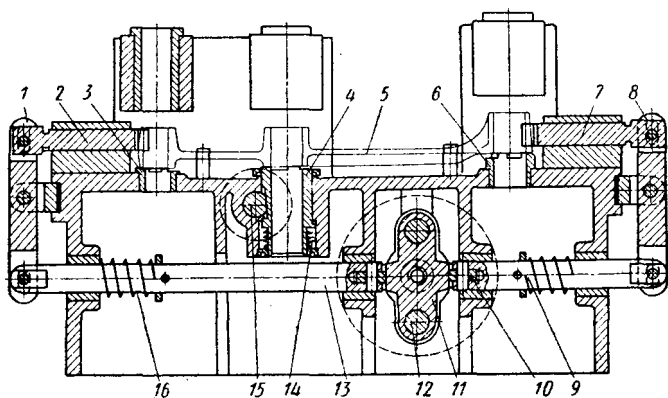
Самоцентрирующее приспособление для обработки рычагов средних размеров
